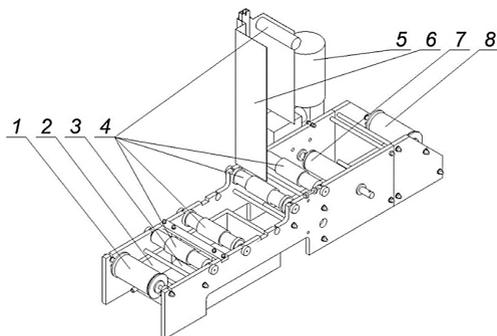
Устройство лабораторной установки для изготовления препрегов:
